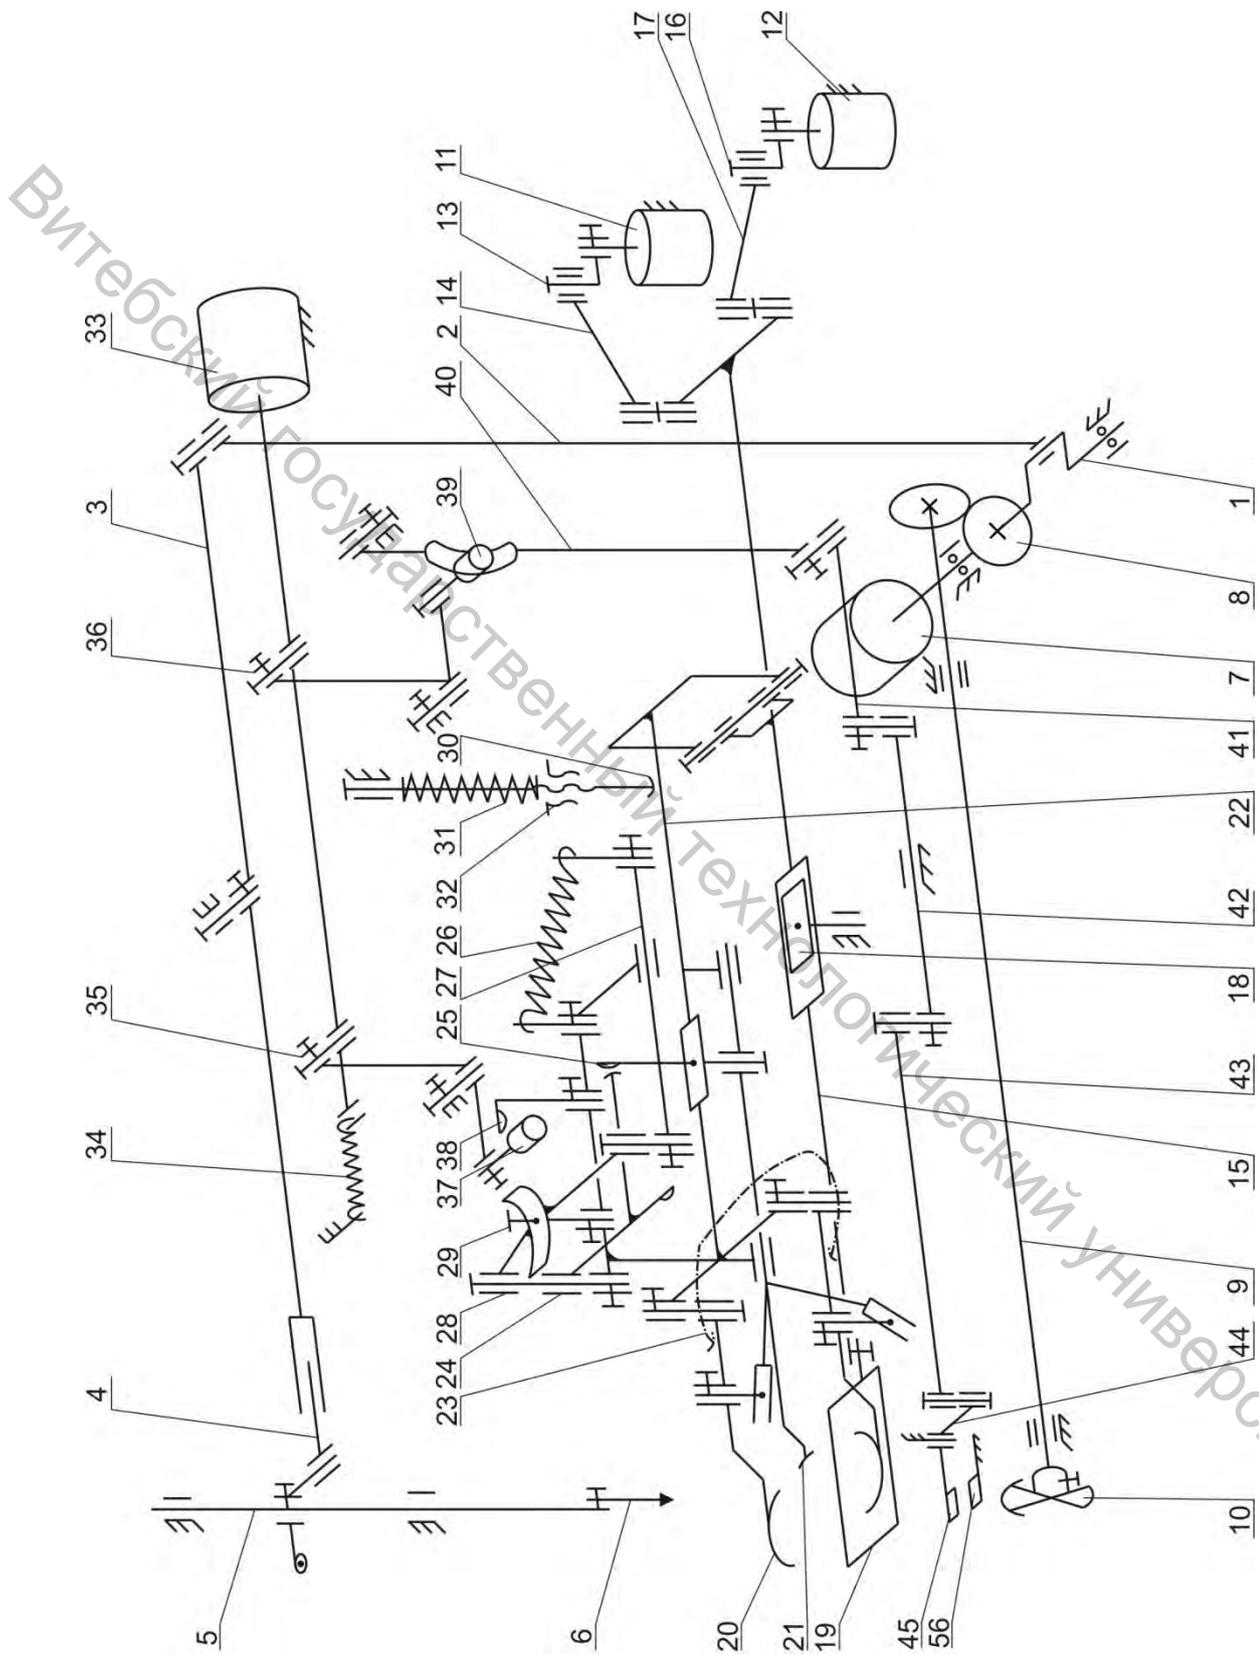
Кинематическая схема полуавтомата MB-1800 класса Juki
